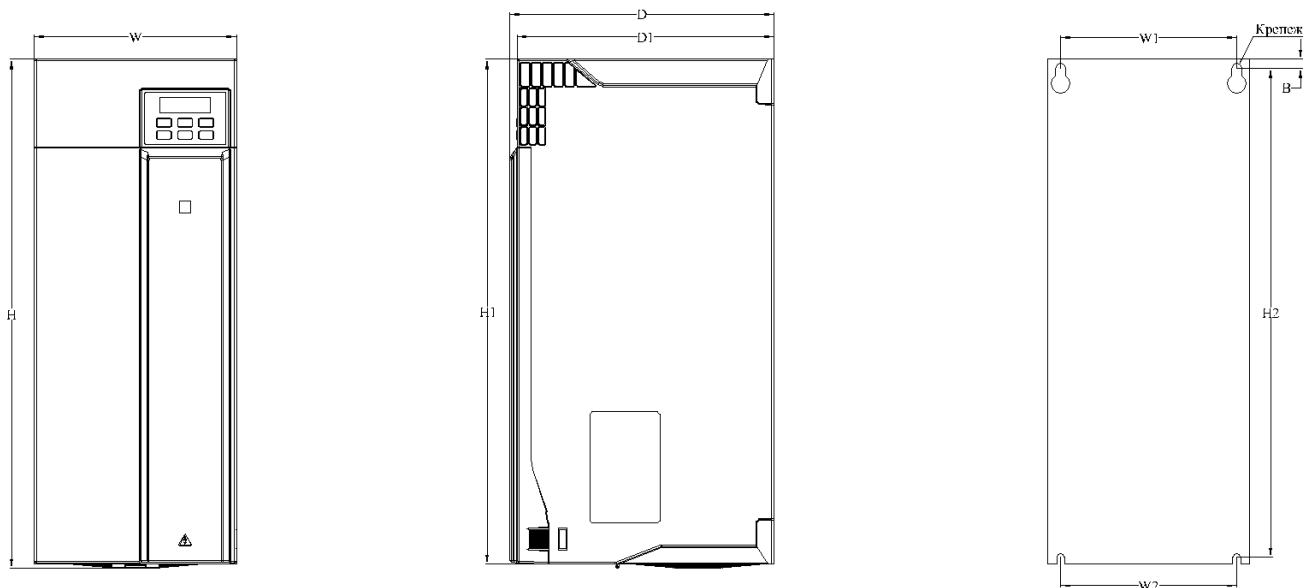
Чертеж преобразователя частоты типоразмер 5
